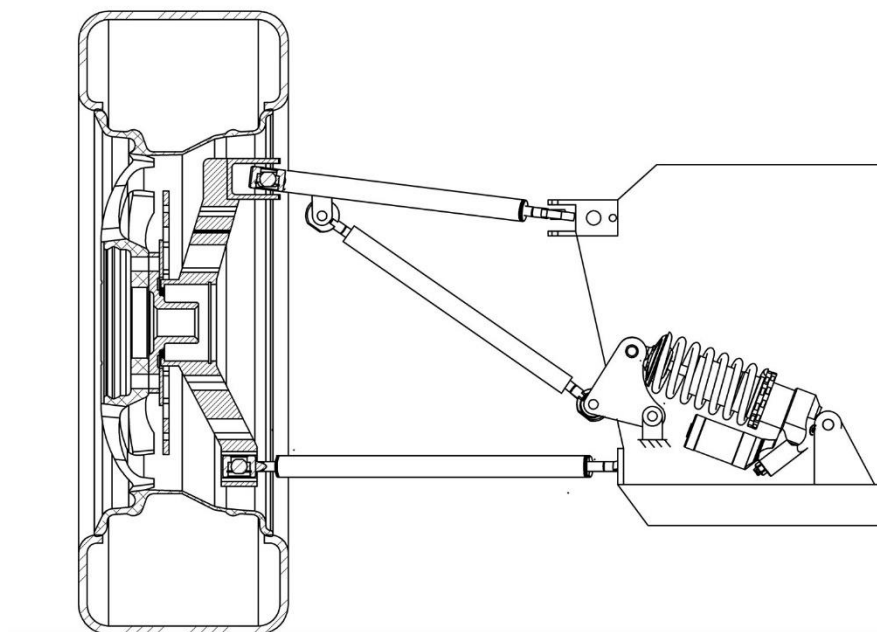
Схема конструкции подвески с тянущей тягой (Pull rod)
